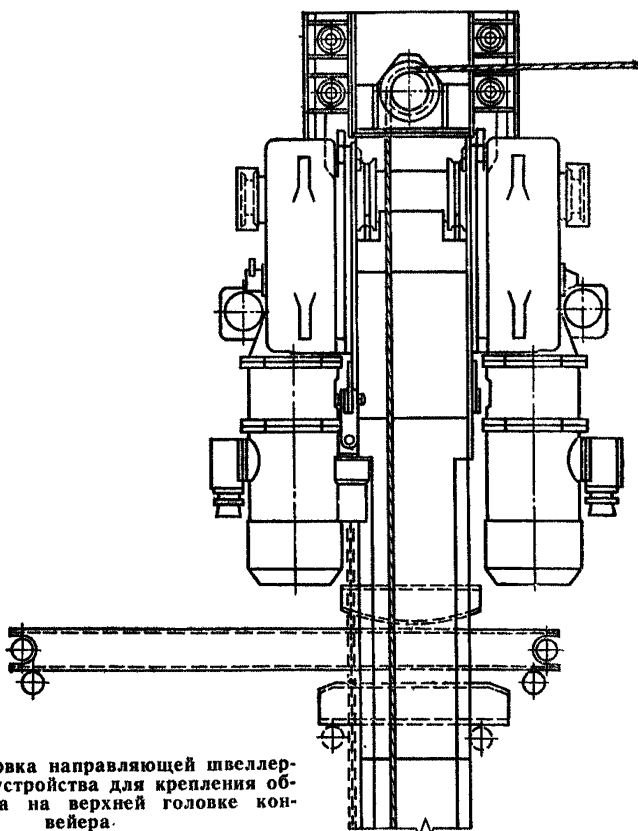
Установка направляющей швеллерной балки и устройства для крепления обводного блока на верхней головке конвейера.
